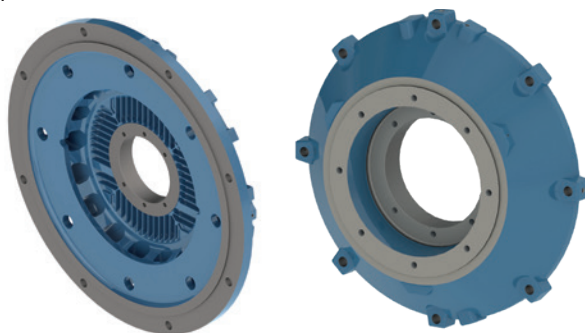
Tampa dianteira – Flange “FF” e Flange “C”.
